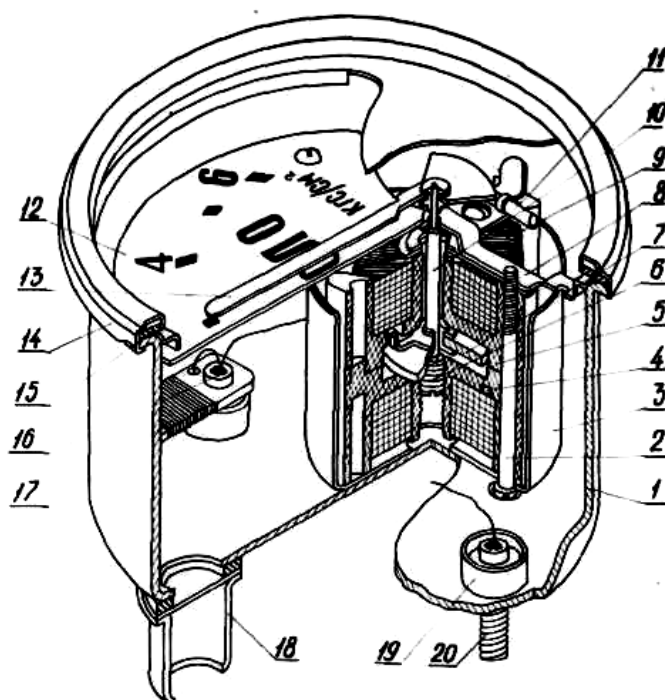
Приемник давления: 1 – корпус прибора; 2 – крепежный винт; 3 – экран; 4 – возвратный магнит; 5 – каркас; 6 – центральный винт; 7 – подвижный магнит; 8 – мостик; 9 – обмотки; 10 – ось магнита; 11 – регулировочный магнит; 12 – шкала; 13 – стрелка; 14 – ободок; 15 – резиновое уплотнение; 16 – клемма батареи; 17 – термокомпенсационное сопротивление; 18 – патрон подсветки шкалы; 19 – изолятор; 20 – клемма датчика
